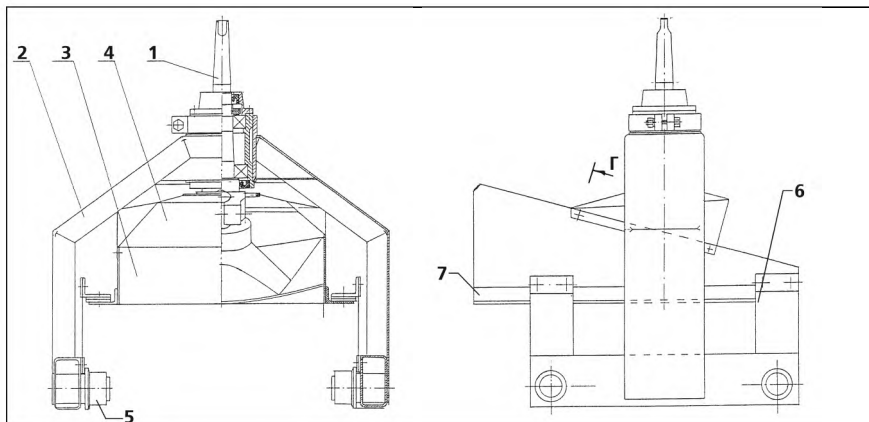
Общий вид нагнетающей насадки. 1 - нагнетатель, 2 - П-образный портал, 3 - бункер, 4 - кожух, 5 - колёса, 6 - пружина, 7 - лыжа.
